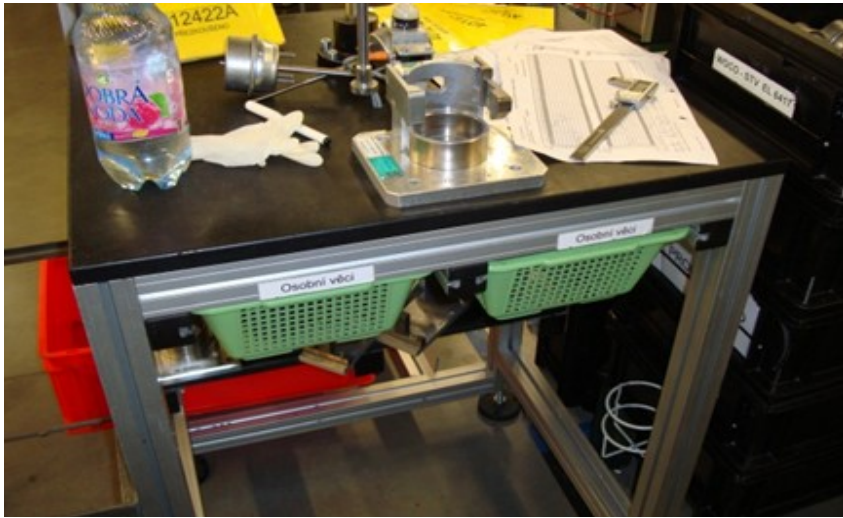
Původní uložení přípravků (vlastní zpracování)
